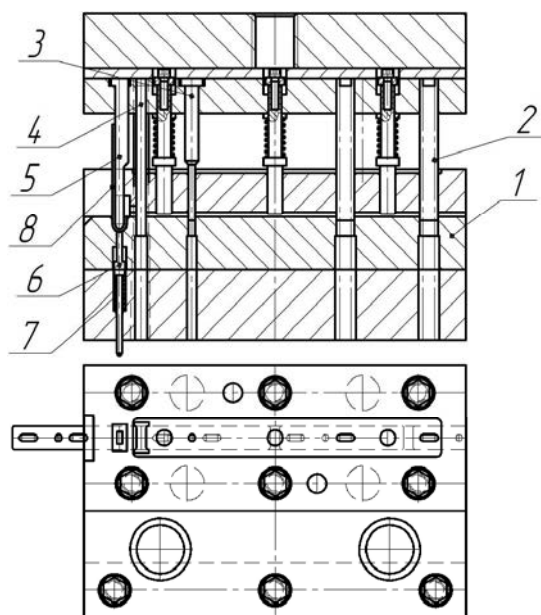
Штамп послідовної дії для виготовлення деталі “Гачок”:
